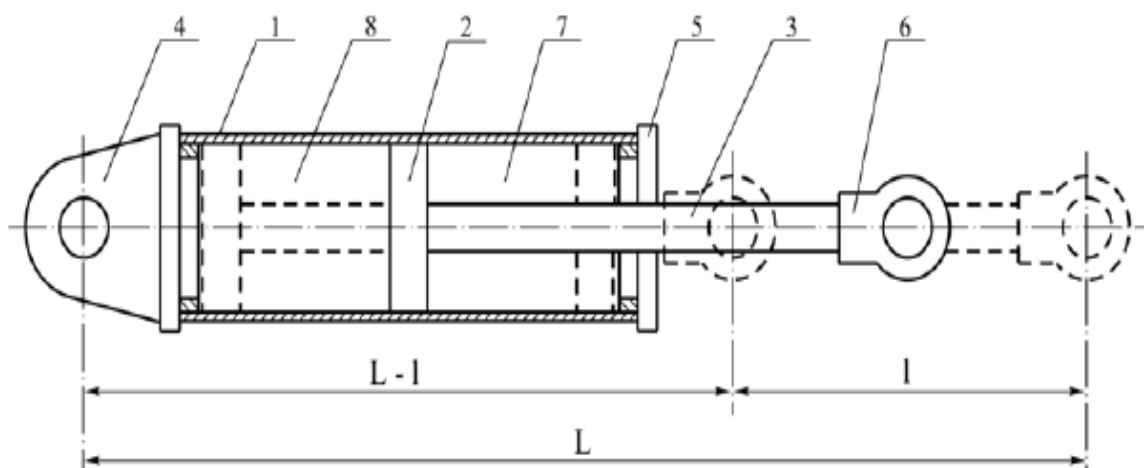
Устройство гидроцилиндра: 1 – цилиндр; 2 – поршень; 3 – шток; 4 – задняя крышка с проушиной; 5 – передняя крышка; 6 – проушина штока; 7 – штоковая полость; 8 – бесштоковая полость
